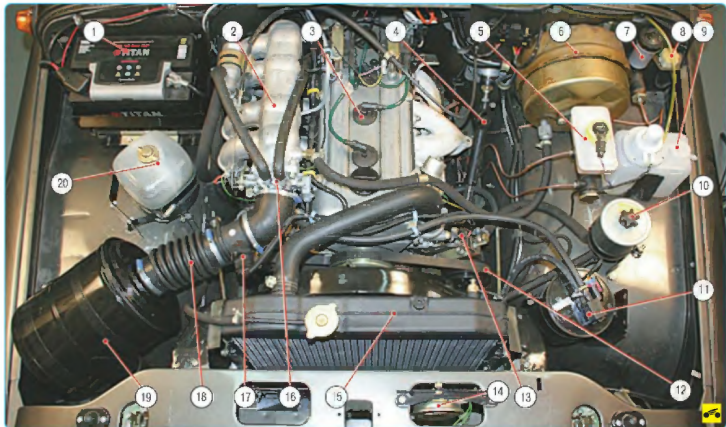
Подкапотное пространство автомобиля с бензиновым двигателем: 1 – аккумуляторная батарея; 2 – ресивер; 3 – двигатель; 4 – рулевой вал; 5 – бачок главного тормозного цилиндра; 6 – вакуумный усилитель тормозов; 7 – бачок гидропривода выключения сцепления; 8 – колодка диагностики системы управления двигателем; 9 – бачок омывателя ветрового стекла; 10 – бачок насоса гидросилителя рулевого управления; 11 – адсорбер системы улавливания паров топлива; 12 – насос гидросилителя рулевого управления; 13 – термостат; 14 – звуковой сигнал; 15 – радиатор системы охлаждения двигателя; 16 – дроссельный узел; 17 – датчик массового расхода воздуха; 18 – воздухоподводящая труба; 19 – воздушный фильтр; 20 – расширительный бачок системы охлаждения двигателя
